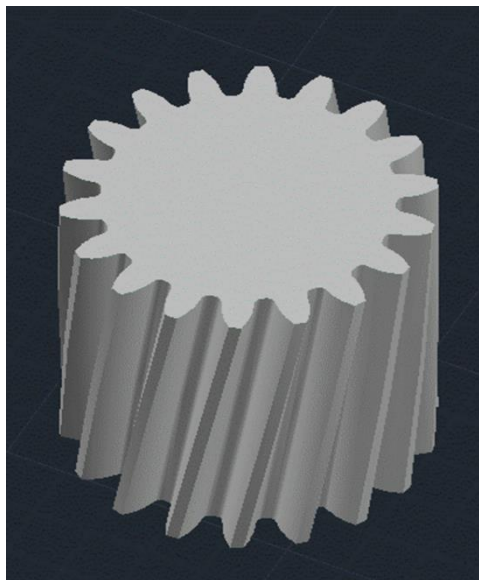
3D модель зубчатого колеса с профилем зубьев упрощенной геометрии
